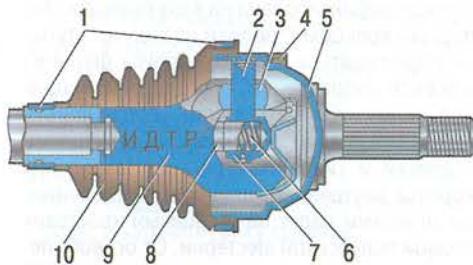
Наружный шарнир равных угловых скоростей GE 86: 1 – хомуты крепления чехла; 2 – трехшпиндельная ступица; 3 – ролик; 4 – зубчатый диск датчика ABS (при наличии ABS); 5 – корпус шарнира; 6 – пружина; 7 – регулировочная проплавка; 8 – толкатель; 9 – вал привода; 10 – чехол шарнира
